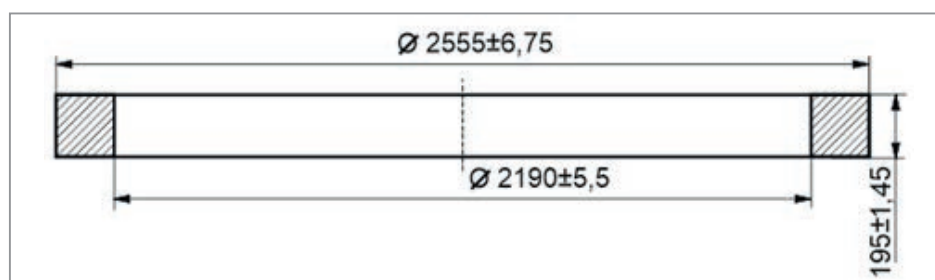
Эскиз окончательной кольцевой заготовки с прямоугольным сечением
